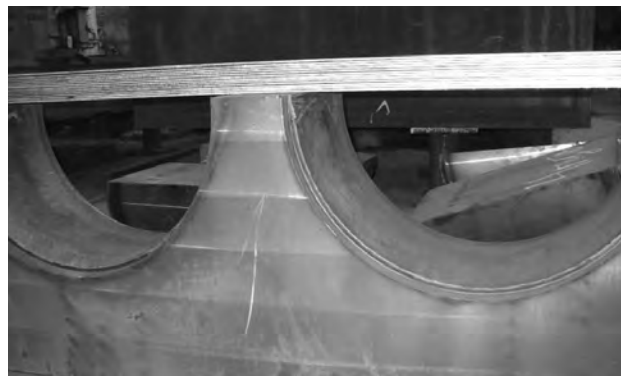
Заготовка корпуса подшипника толщиной 450 мм с вырезанными полукруглыми карманами
